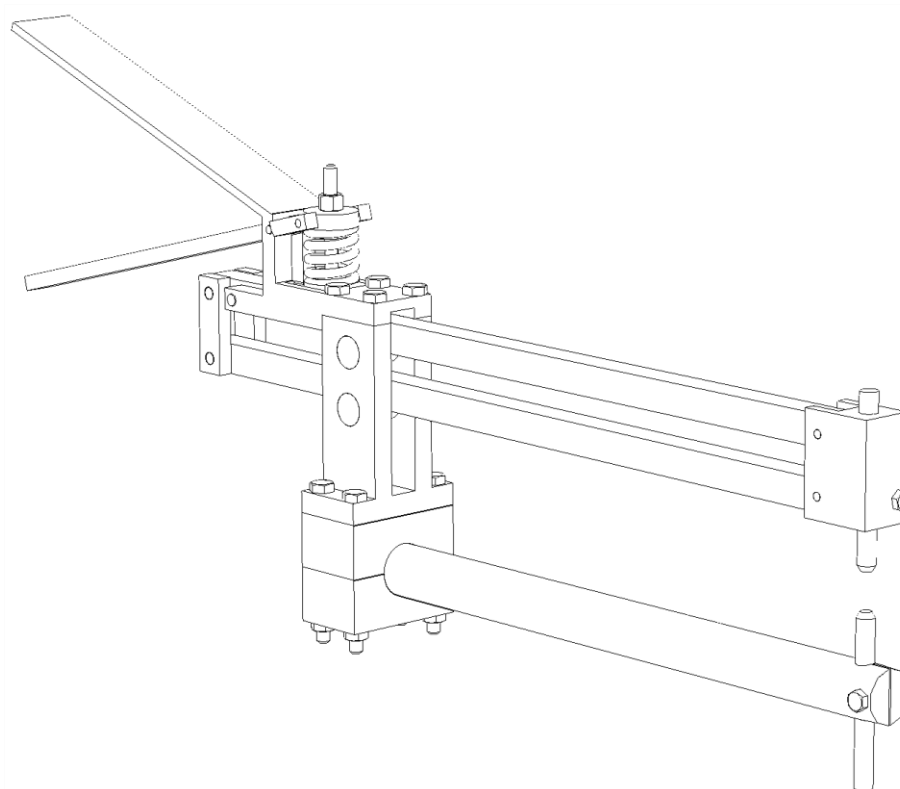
Клещи для контактной точечной сварки в сборе.
